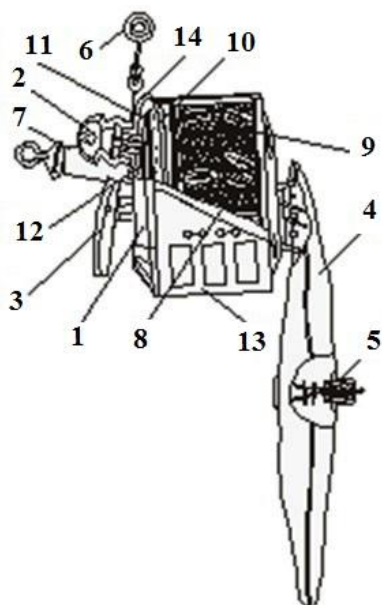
Шахтный изолирующий малогабаритный самоспасатель ШСМ-30
